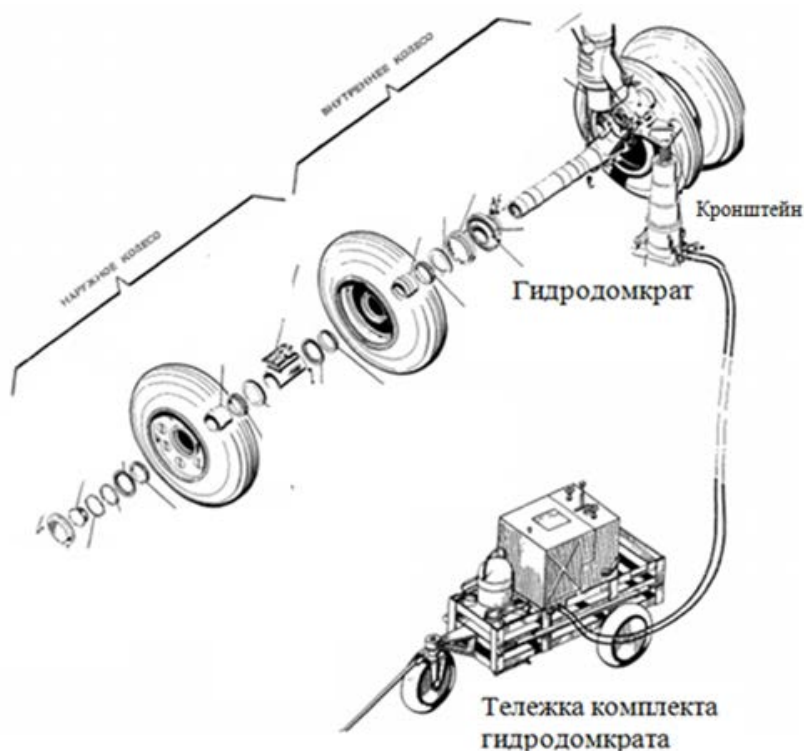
Снятие и установка колес носовой ноги шасси самолета Ил-76
